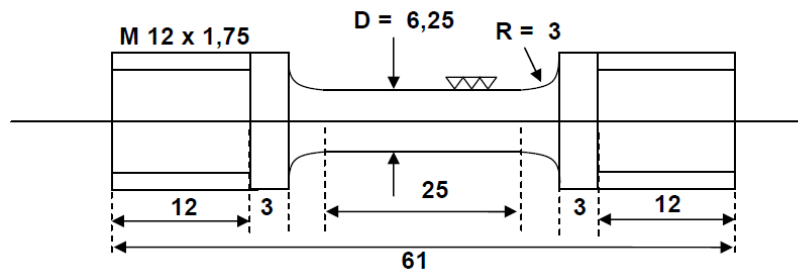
Géométrie des éprouvettes de fluage [Bue13].
